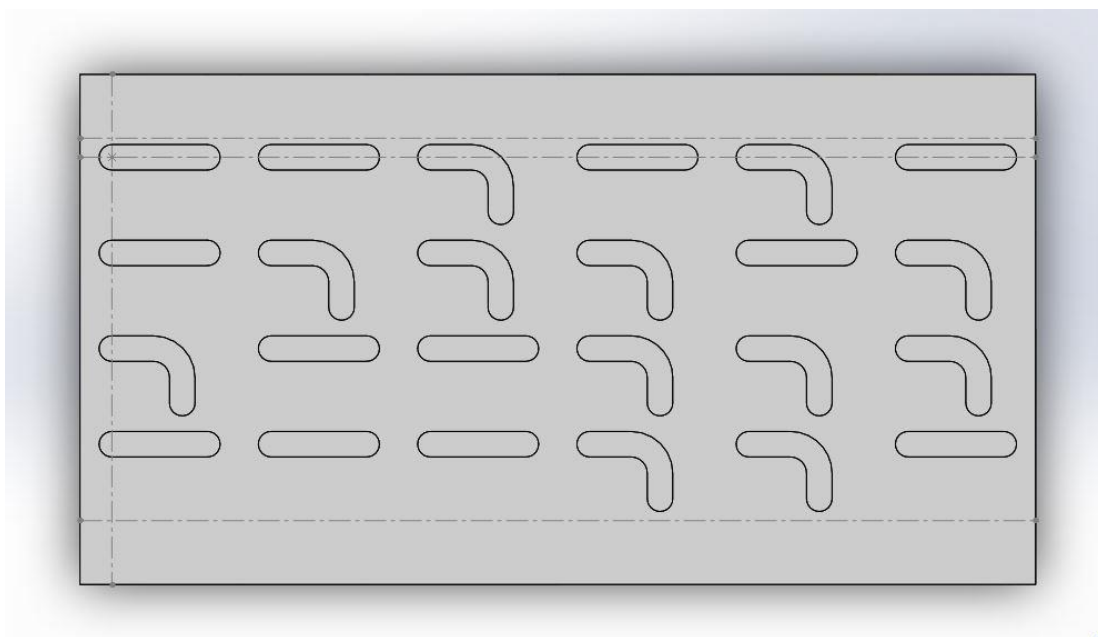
CAD de los ensayos a realizar (herramienta de 4 mm).
